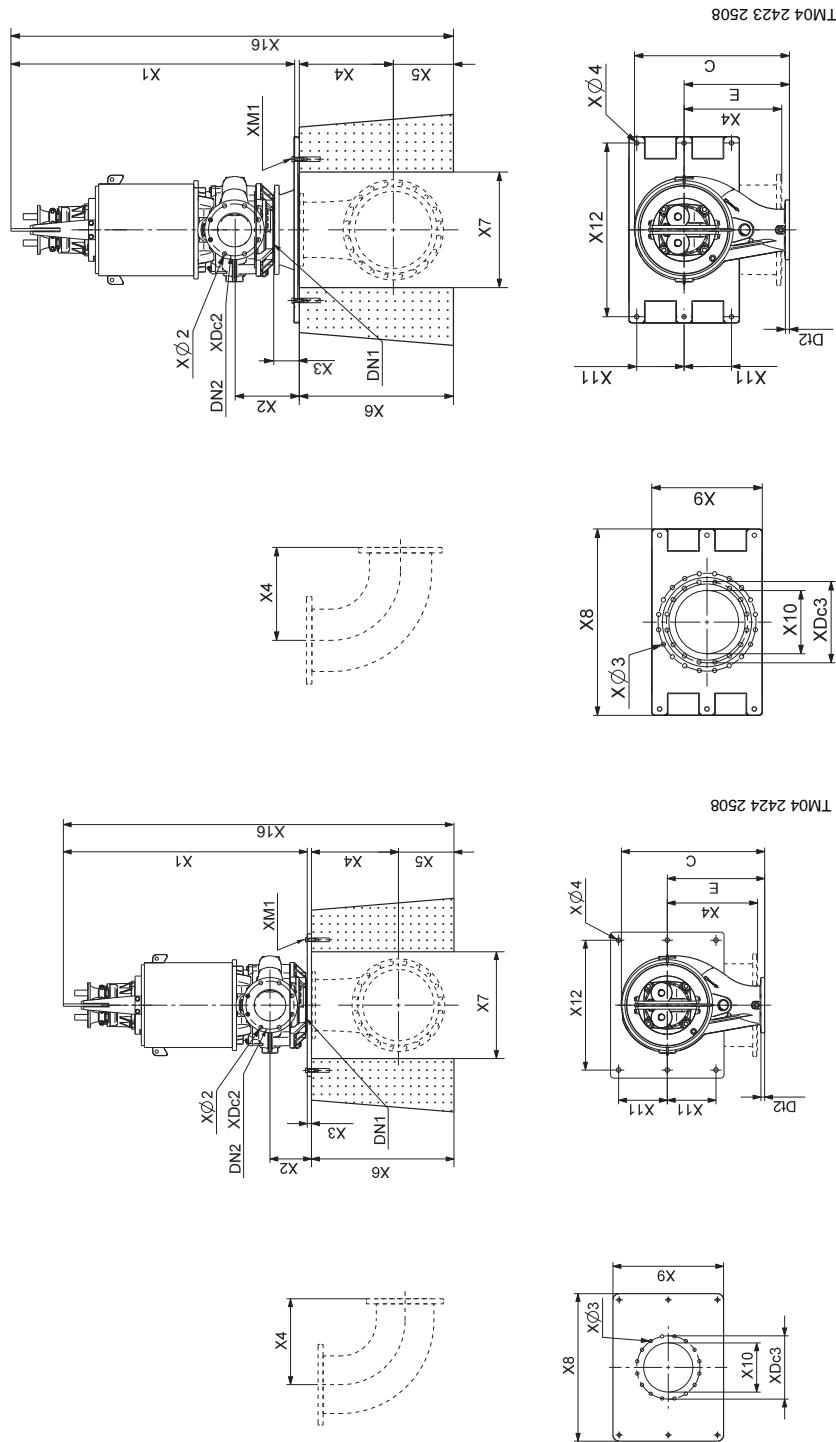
Габаритные размеры, сухая вертикальная установка на бетонном основании
